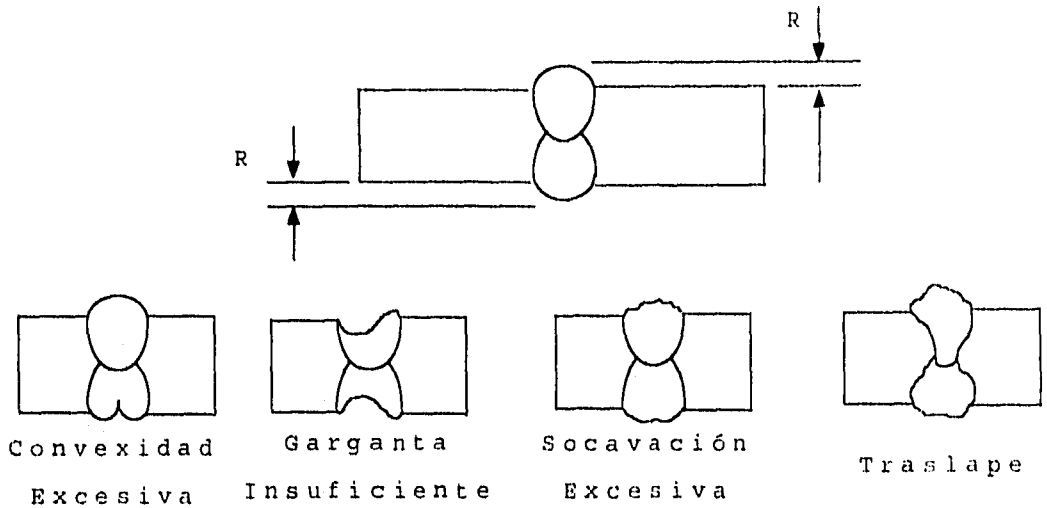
Cortes de soldadura de ranura aceptables e inaceptables.
